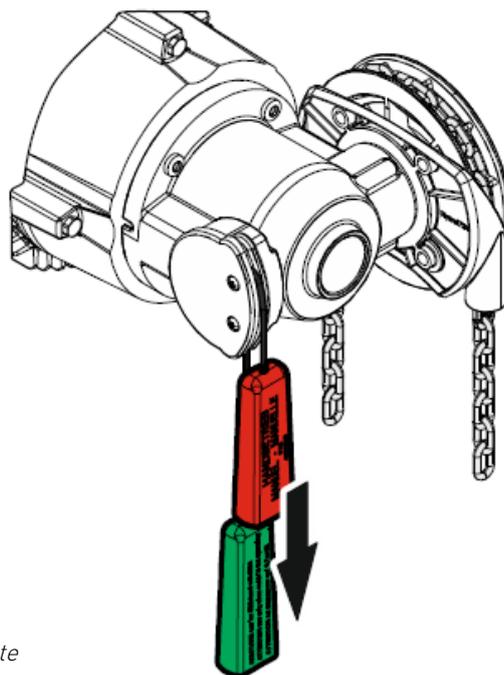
Detailskizze zum Entsperren mit Kette
